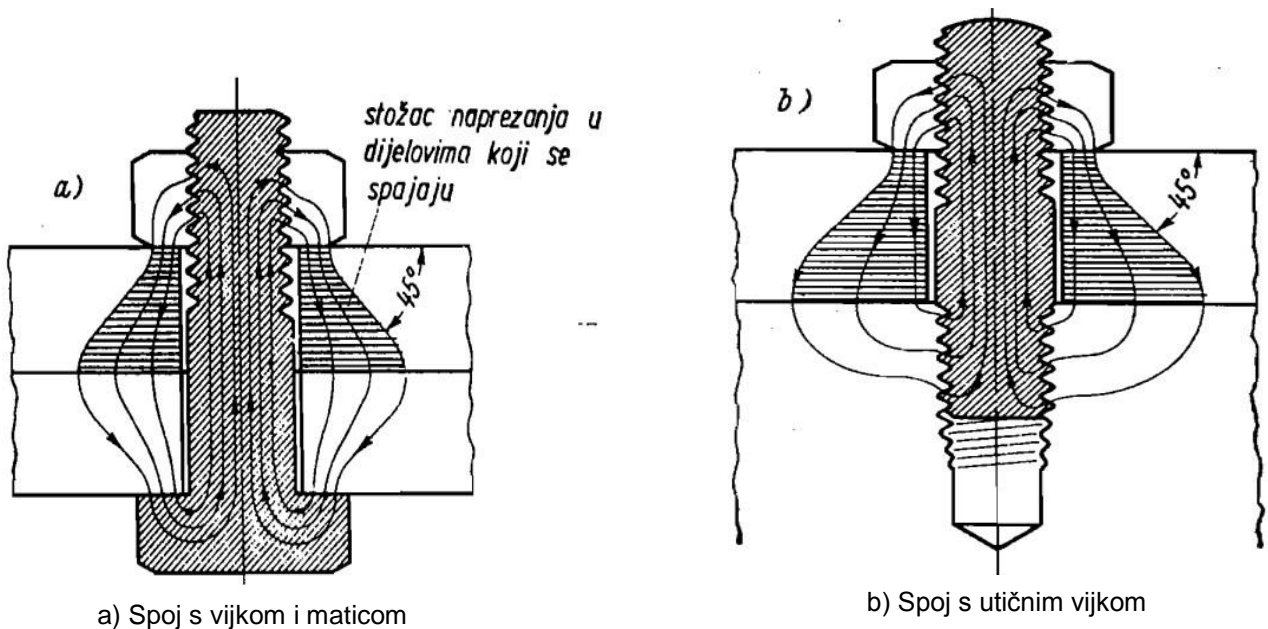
Vijčani spojevi konstrukcija ([13], str 89)
